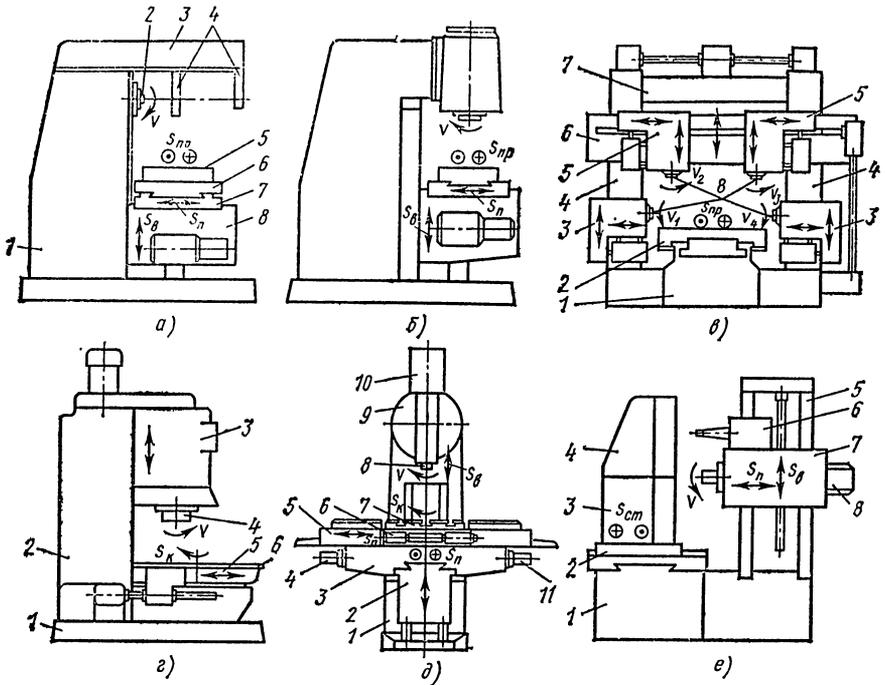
Основные типы фрезерных станков (стрелками показаны установочные движения частей станка)
